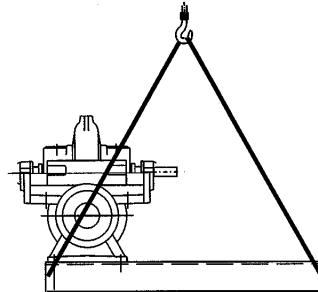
Транспортировка насосного агрегата (без двигателя)
